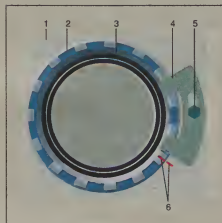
Регулировочная гайка главной передачи "Москвича-2141". 1 - картер; 2 - гайка; 3 - сальник; 4 - стопорная пластина; 5 - болт крепления стопорной пластины; 6 - метки.
